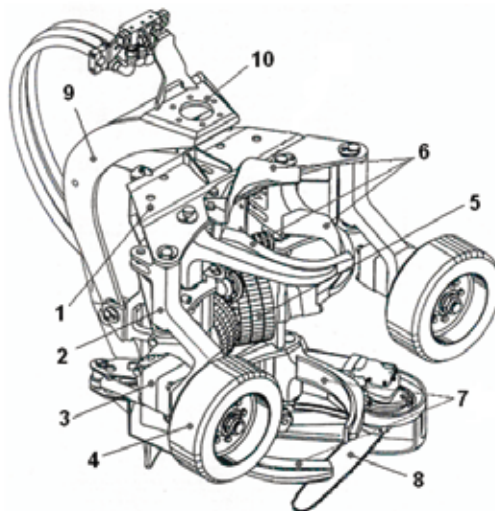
Харвестерная головка: 1 – корпус; 2 – захваты вальцов; 3 – высокомоментные гидравлические моторы; 4 – протаскивающие вальцы; 5 – два неподвижных (фиксированных) вальца с высокомоментными гидравлическими моторами; 6 – верхние сучкорезные ножи; 7 – нижние сучкорезные ножи; 8 – пильный механизм; 9 – скоба наклонного механизма; 10 – площадка для крепления поворотного ротора
